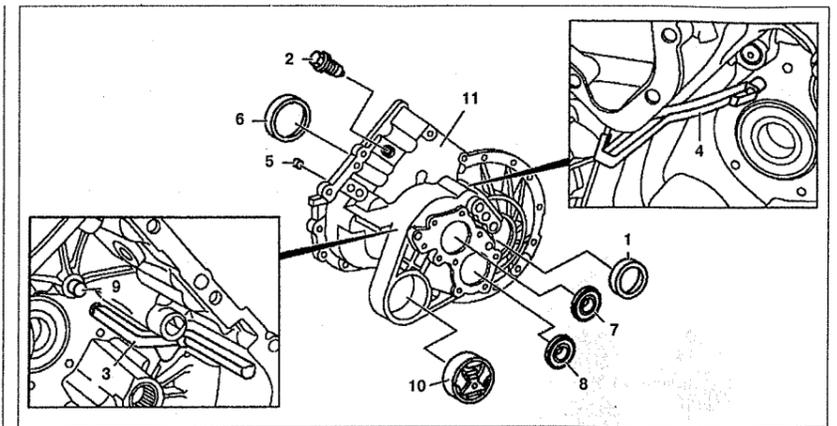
Корпус коробки передач (автомобили с двигателями 611.980):
